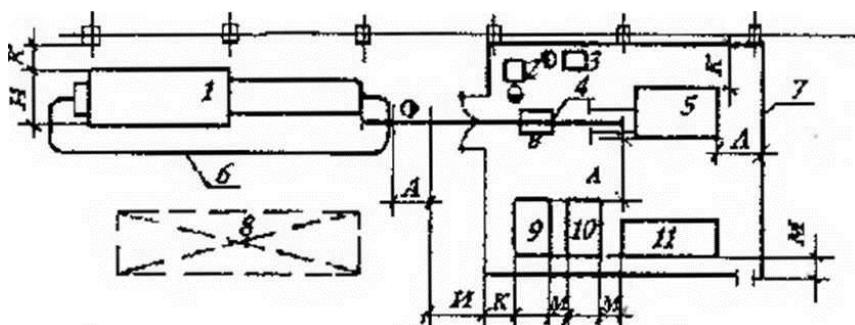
Размещение установок автоматической сварки и резки с поворотными колоннами и самоходными порталами:] - портал самоходный; 2 - автомат сварочный или резак; 3 - универсальный цепной кантователь или стол термической резки; 4 - место складирования; 5 - стэнд; 6 - роликовый стэнд; 7 - кантователь; 8 - поворотная колонна
